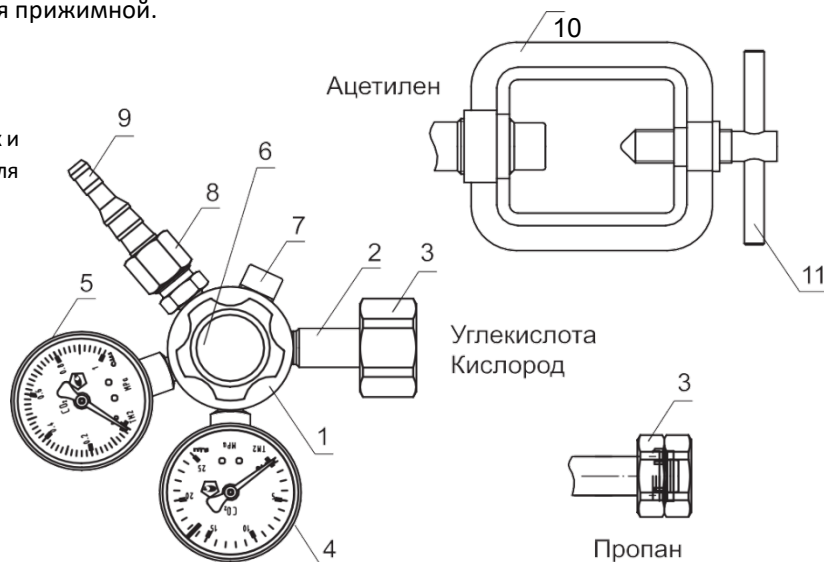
УСТРОЙСТВО РЕДУКТОРА
